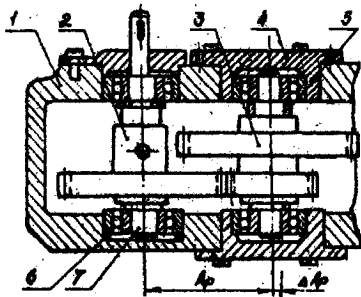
, б. Схема редуктора з регулювальними втулками
